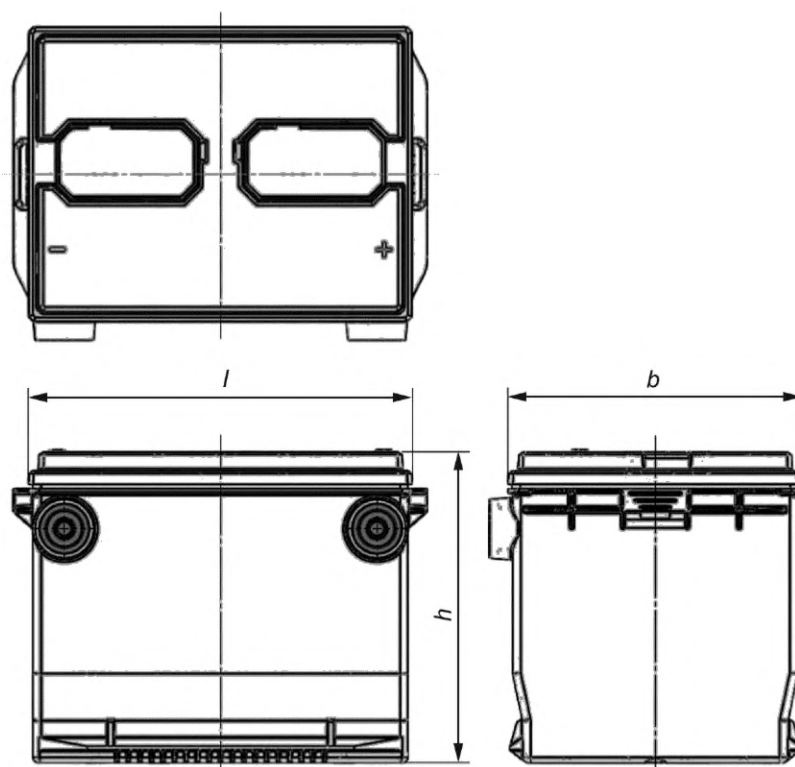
Основные размеры батарей типоразмеров 75, 78, 100 с положительным боковым выводом, расположенным на корпусе батареи справа
